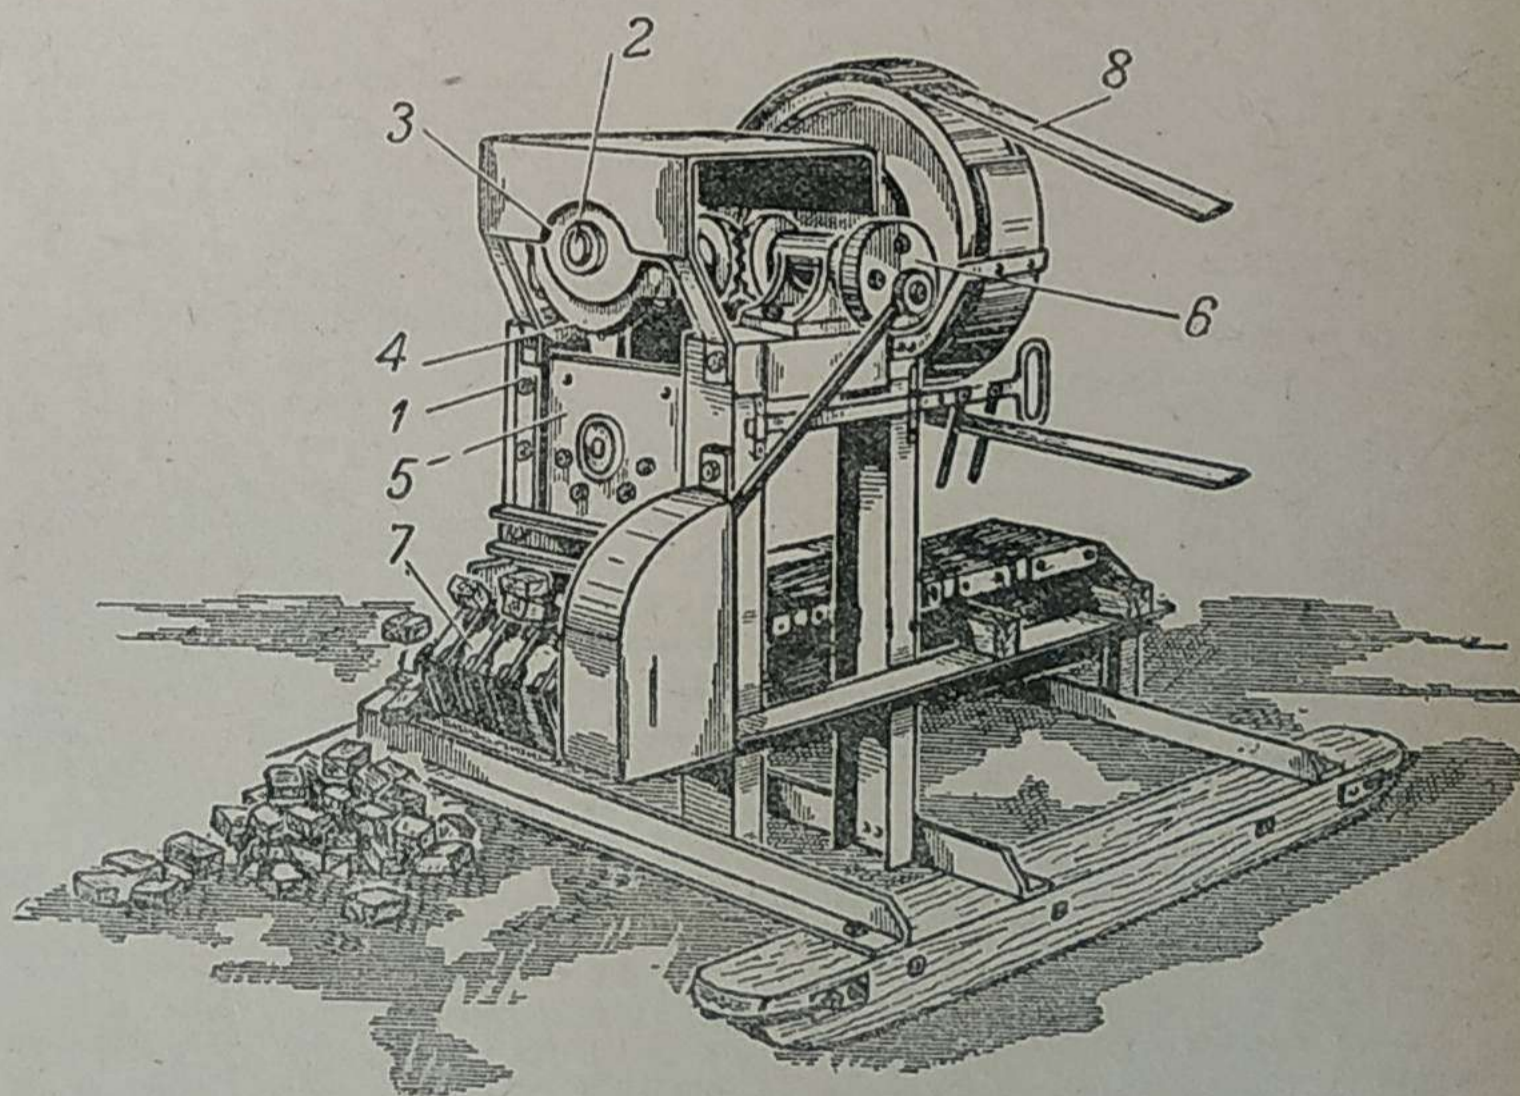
Общий вид колуна конструкции гг. Лебедева и Назарова.
